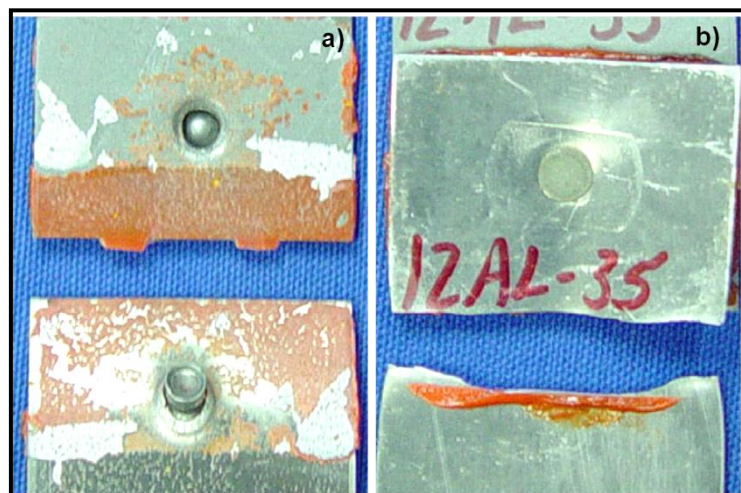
Fractura a fatiga en uniones remachadas, a) arrancamiento del remache, b) fractura en la lámina de la junta [49].
